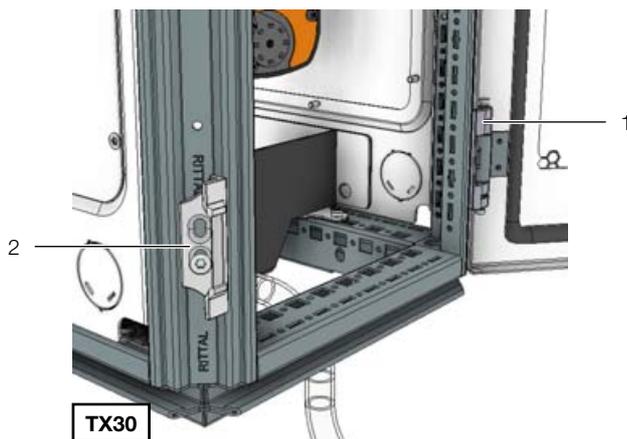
Befestigungselemente am Liquid Cooling Package – Rückansicht
